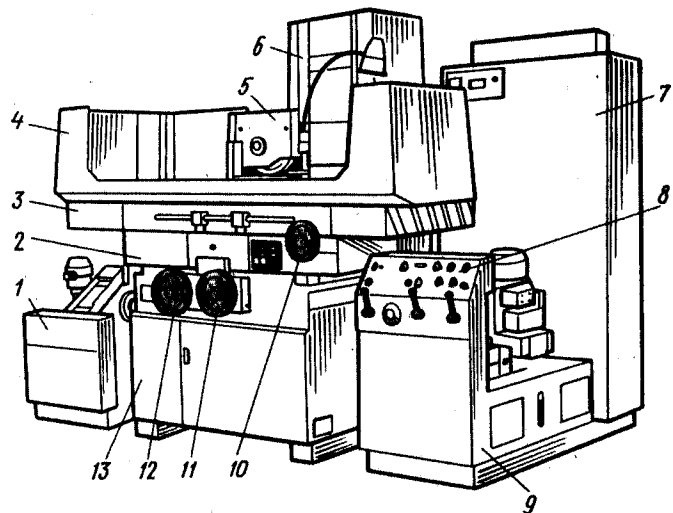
Плоскошлифовальный станок с прямоугольным крестовым столом и горизонтальным шпинделем
